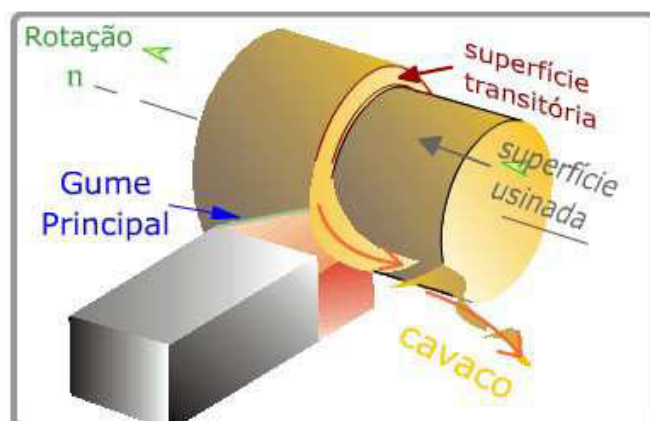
Rotação - Superfície transitória - Superfície usinada - Gume principal - Cavaco
